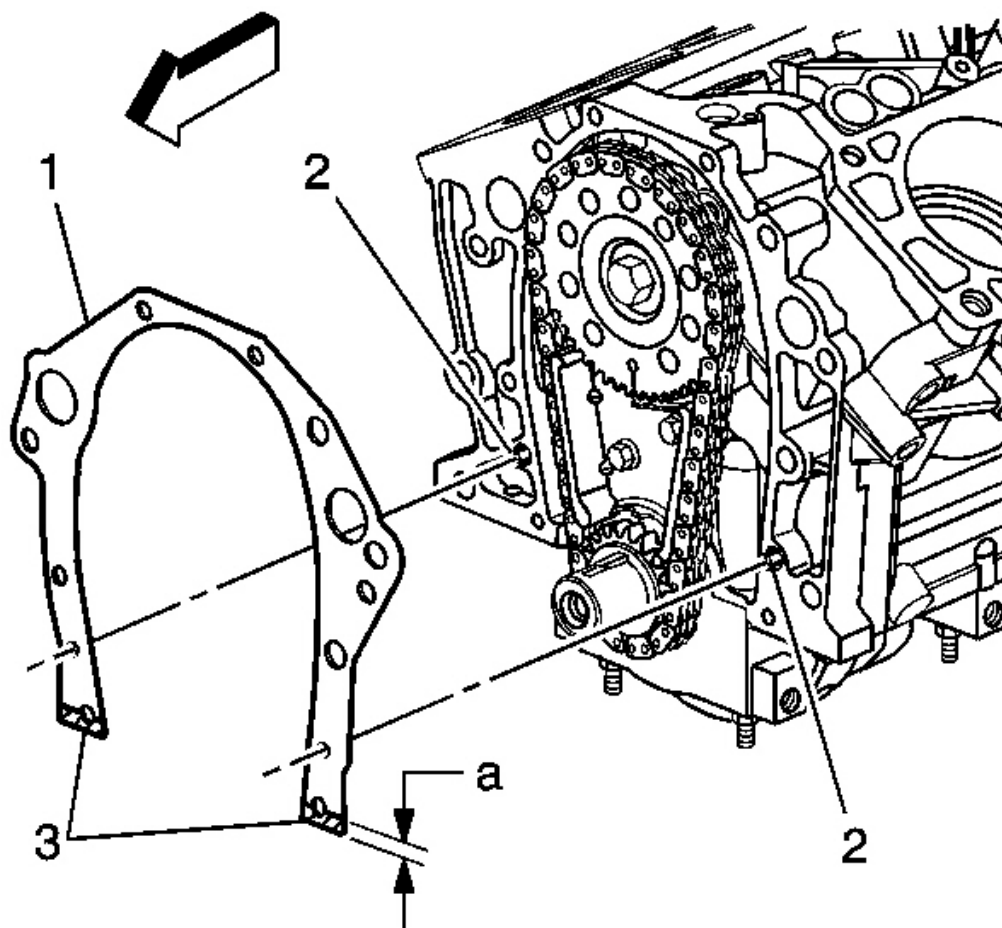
Vista de la cubierta del motor delantero y pernos
